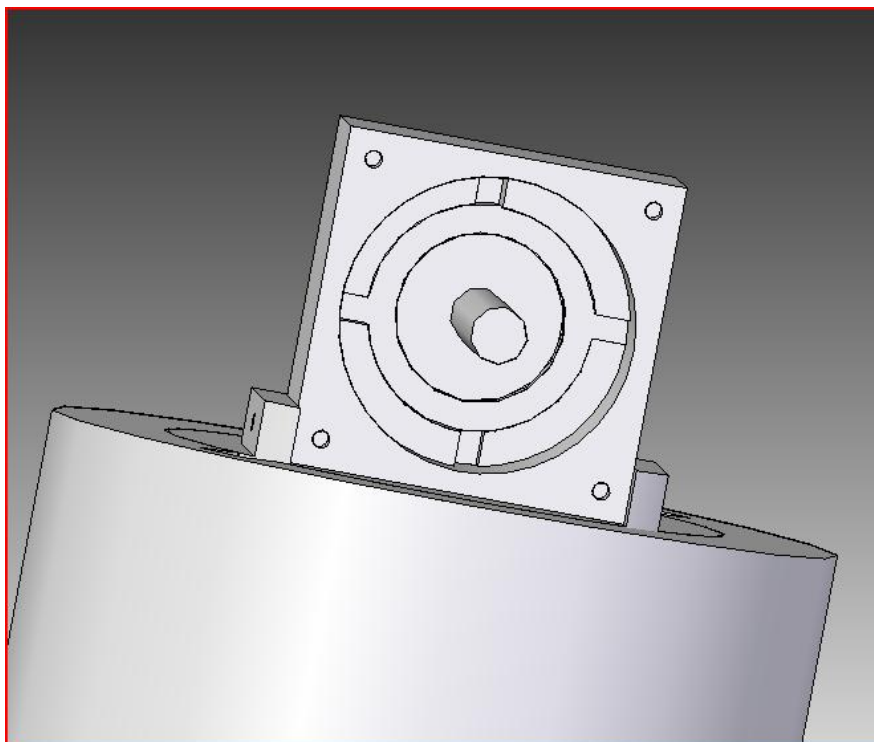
Diseño en Solid Edge. Mecanismo del giro superior
